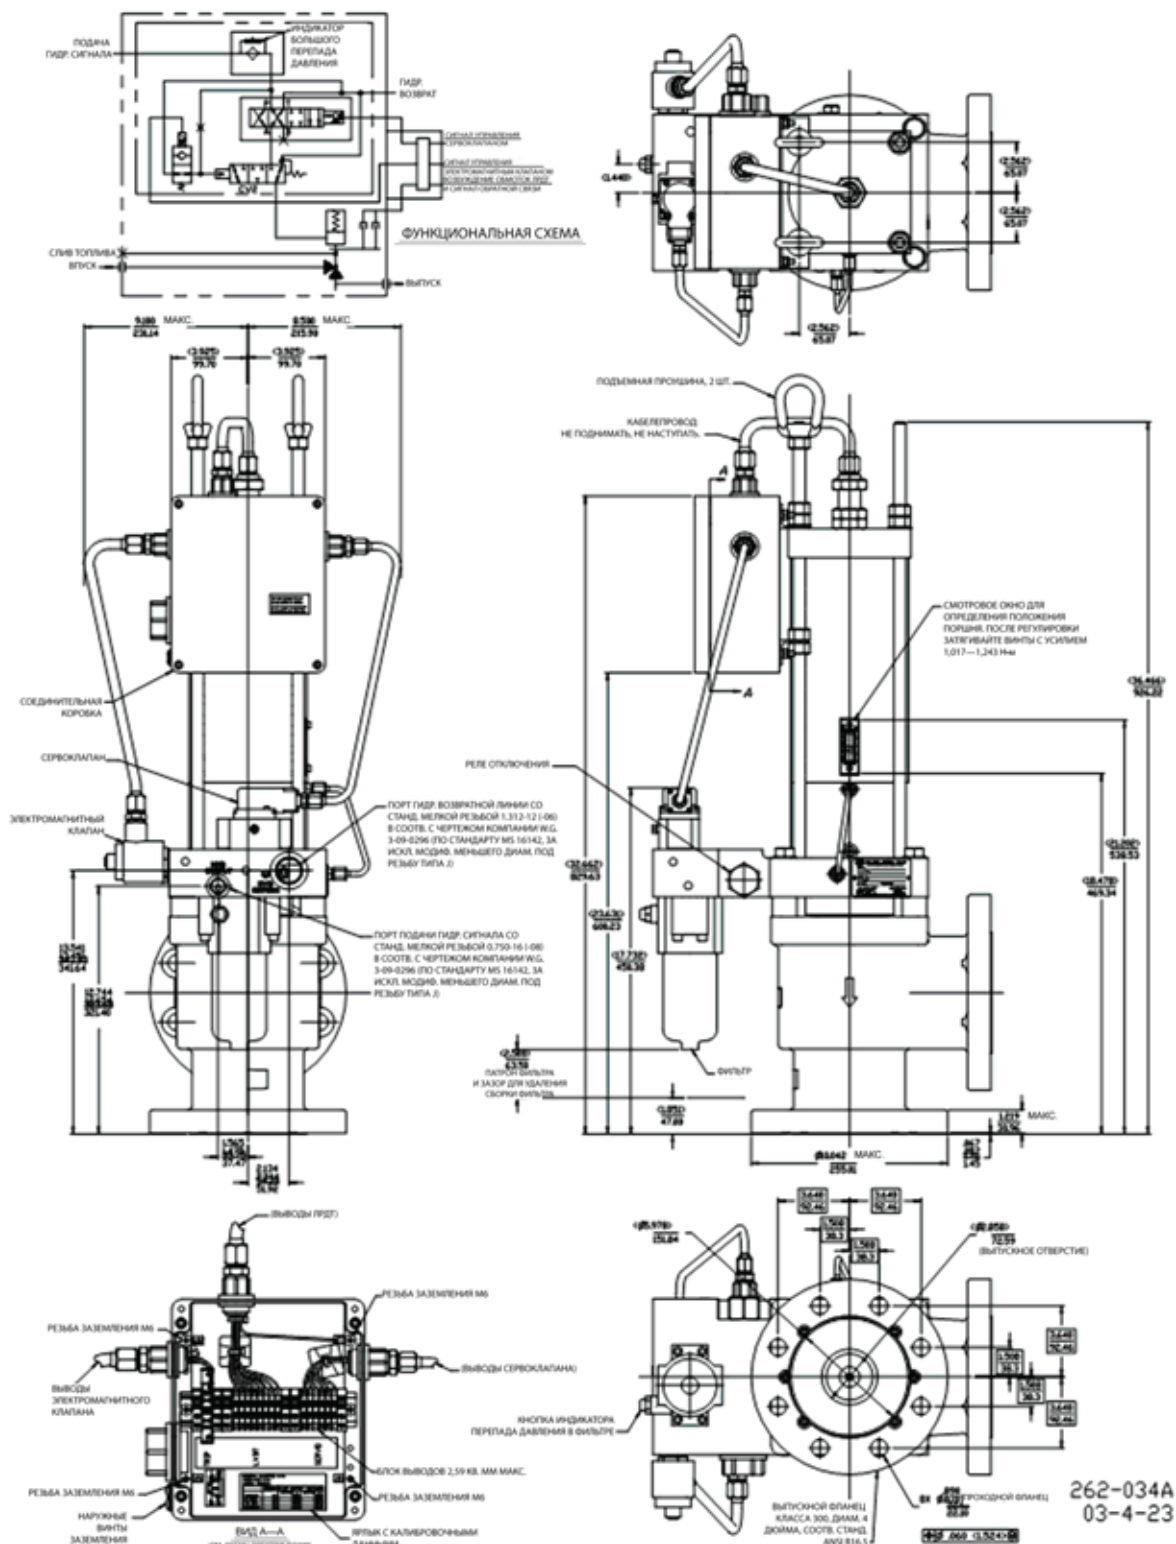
а. Контурный чертеж регулятора (4 дюйма, одноотверстная соединительная коробка)
